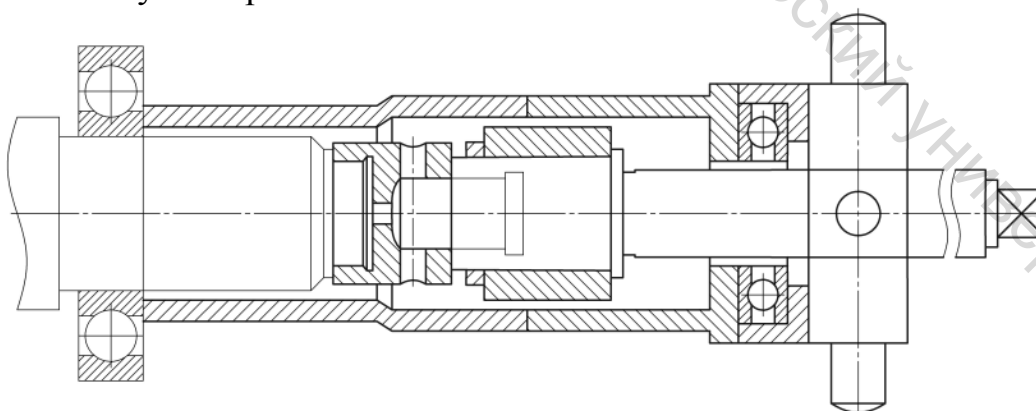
Напрессовка подшипников качения на вал с помощью винтового приспособления со сменными деталями
